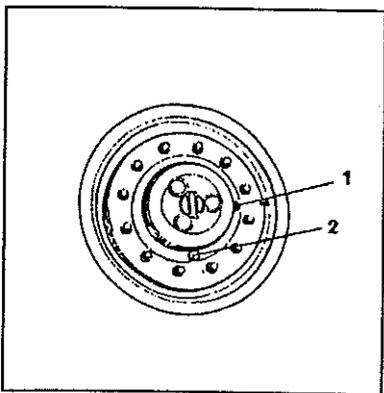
Engranaje planetario-posición de llenado de aceite
